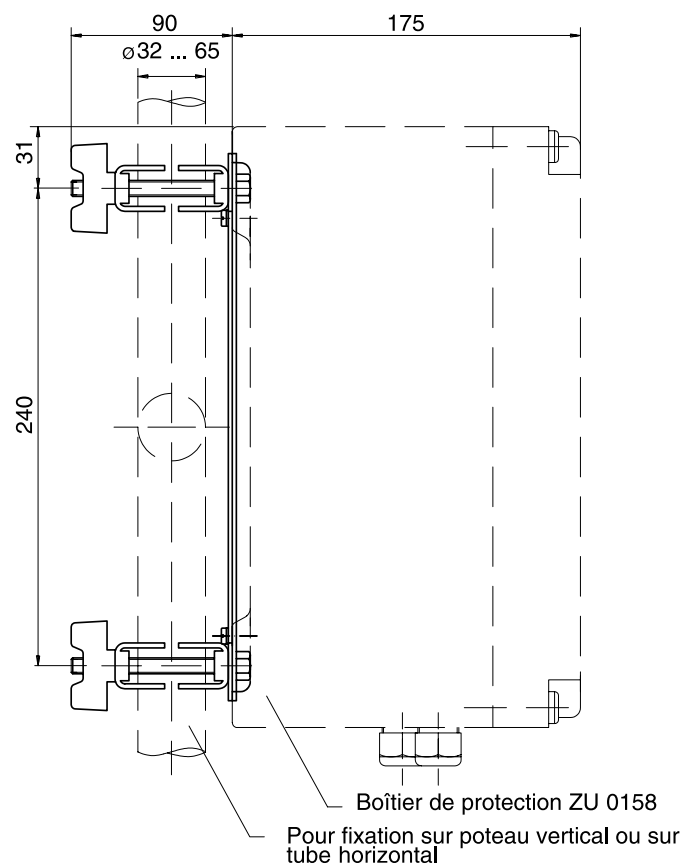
Jeu de colliers pour fixation sur mât ZU 0220 pour boîtier de protection ZU 0158
